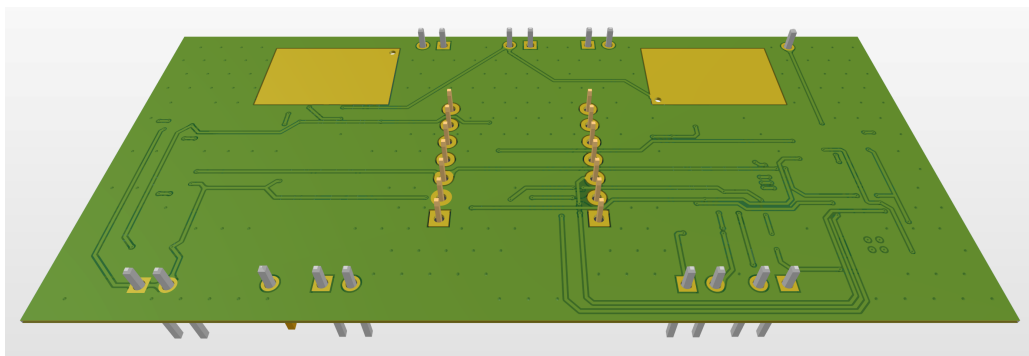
Vista 3D inclinada de la cara inferior del PCB.
